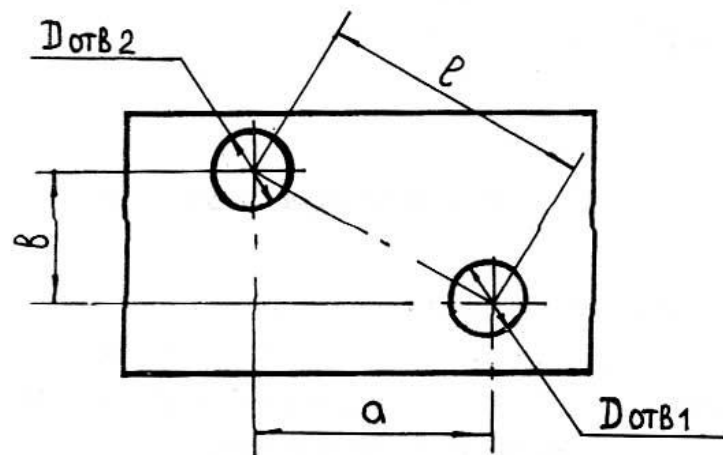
Схема установки заготовки отверстиями на два пальца
